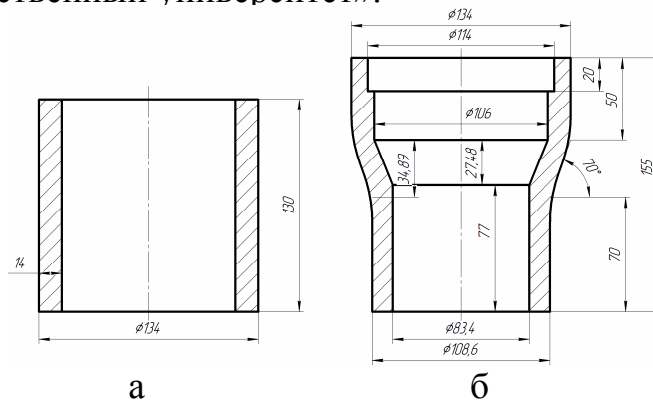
Схемы заготовки (а) и детали «переходник» (б)
